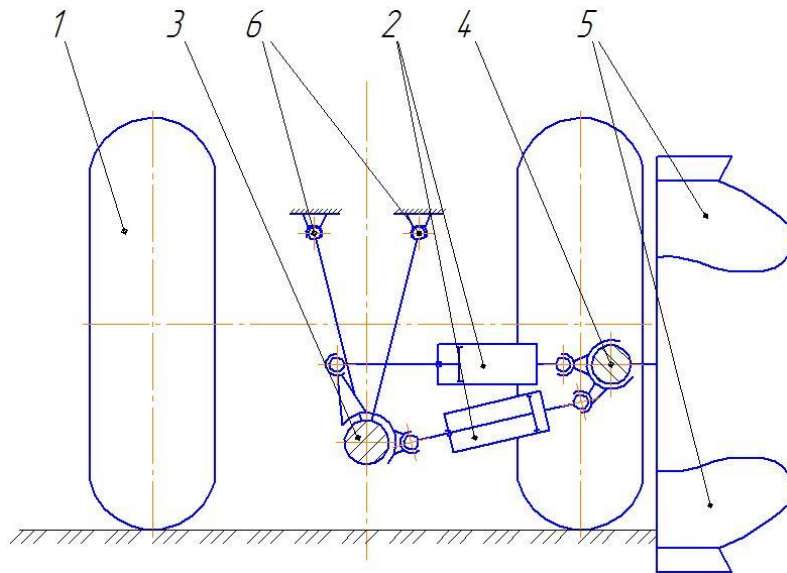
Поворотний механізм плуга фірми "Lemken"
